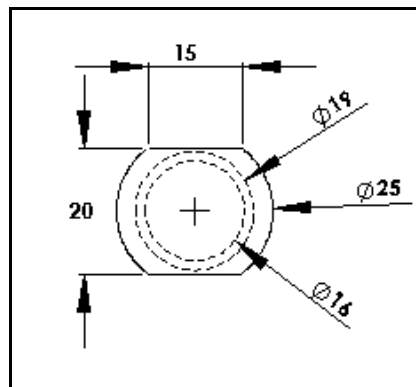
14 Dimensiones de la probeta en mm, vista lateral
